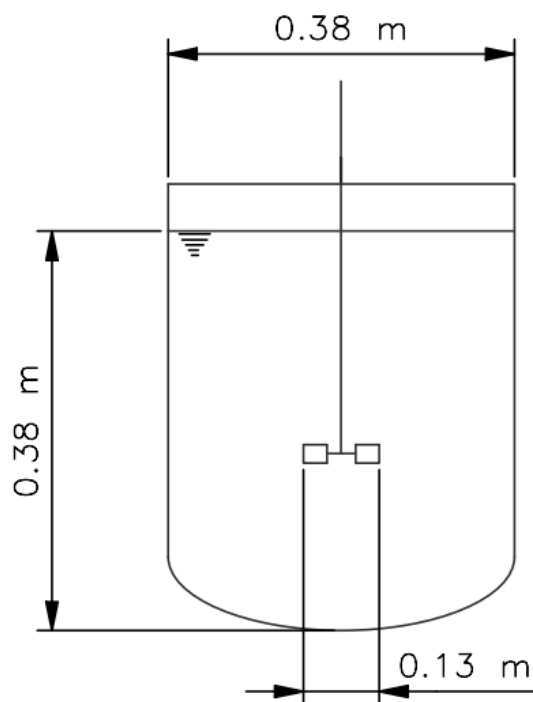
Dimensionamiento inicial del tanque interno para un agitador de palas planas.
